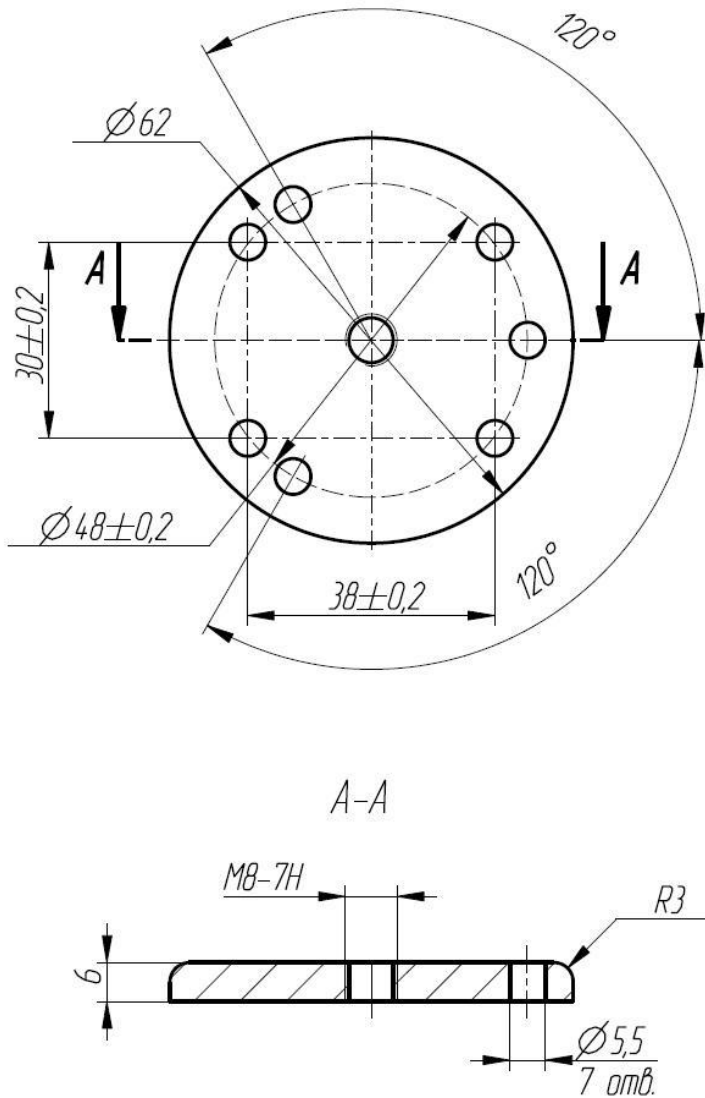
Габаритные и присоединительные размеры сферы для крепления БИ04.42-01
